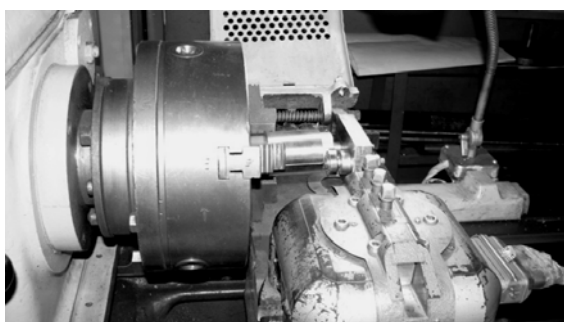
Фотографии устройства для отрезки трубчатых заготовок
